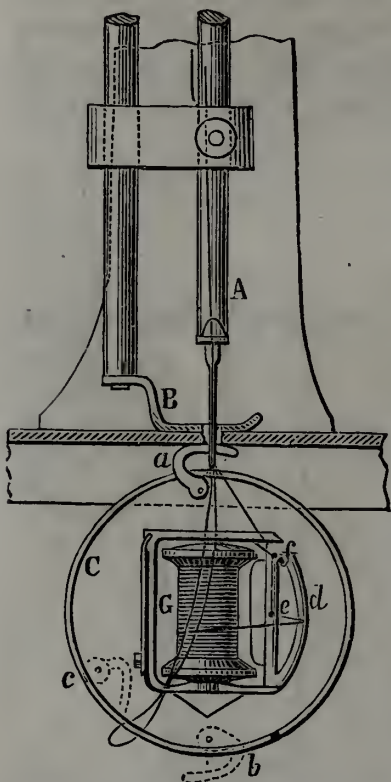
Machine de MM. Huartu et Hautin. Élévation.
